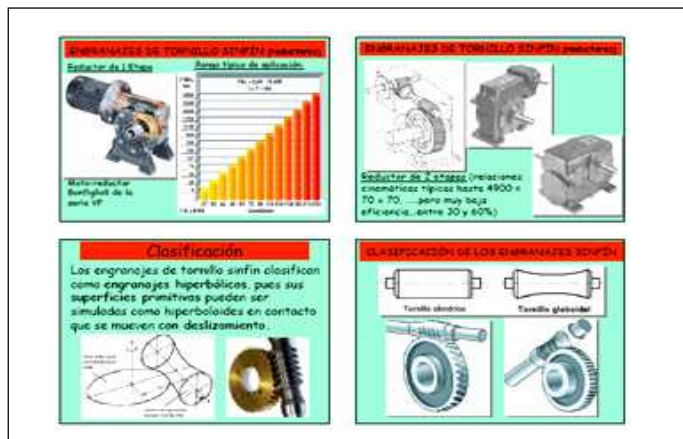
Imagen para explicar soluciones constructivas en engranajes de tornillo sinfín.
